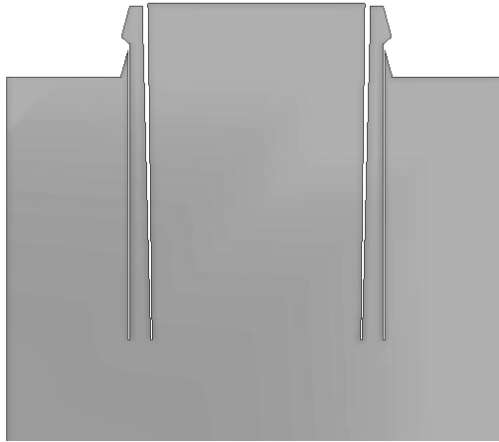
Dettaglio dei Cantilever Beams incassati.
